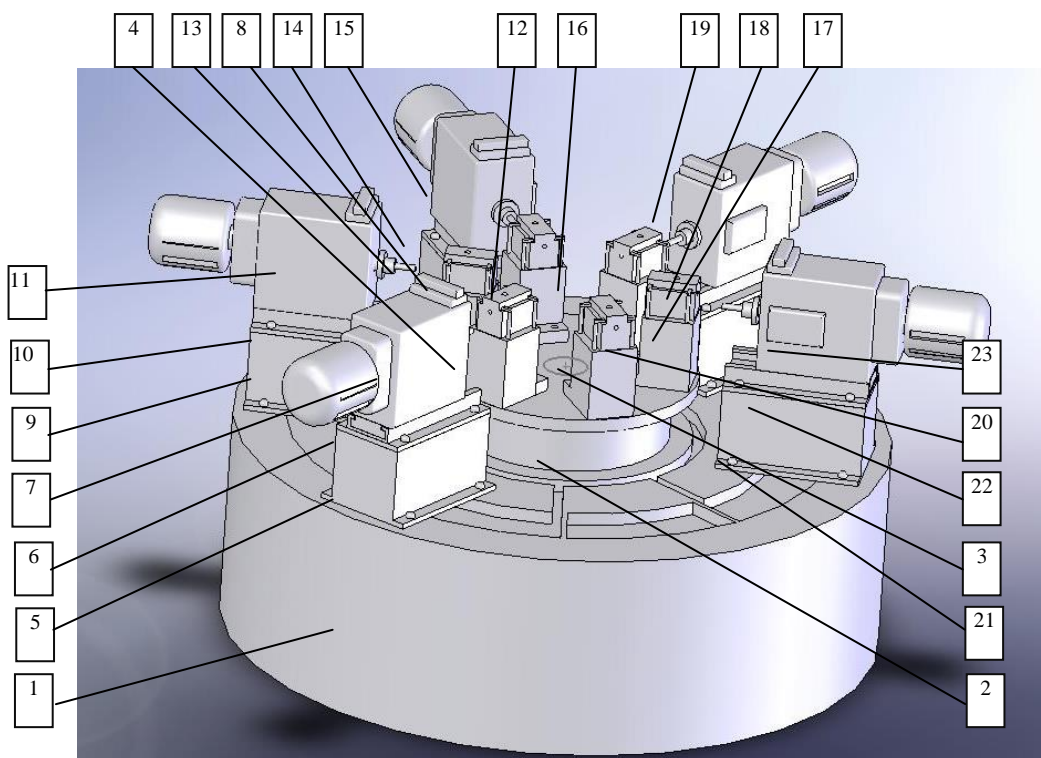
Агрегатный станок с пятью рабочими позициями.
